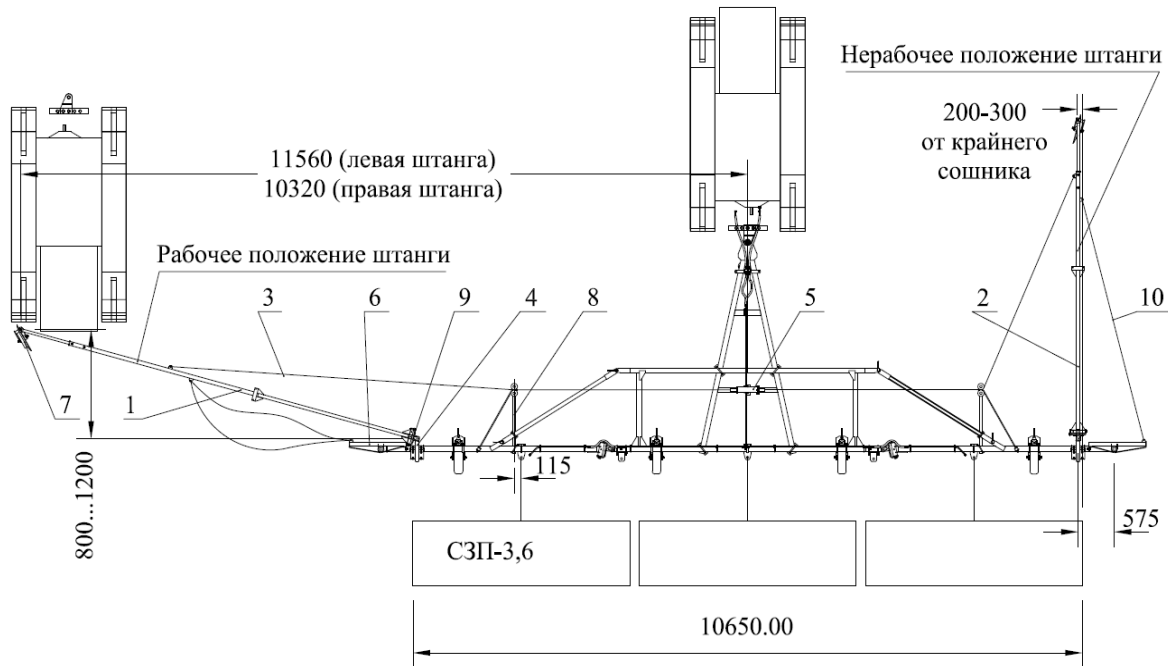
Схема установки маркера для 3-х сеялочного агрегата.
